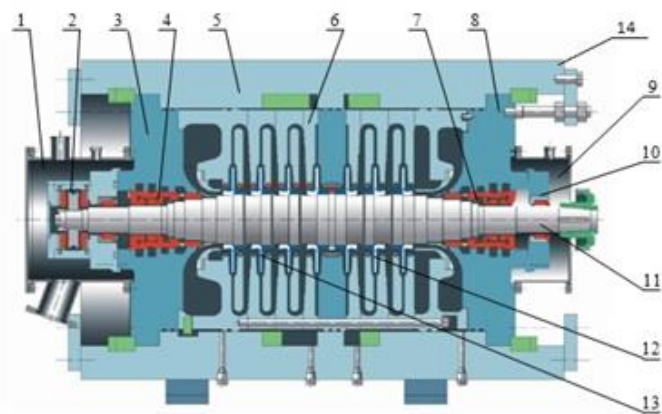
Конструкція відцентрового вакуум-компресора. 1, 9 – кожух, 2 – підшипник опорно-ударний, 3, 8 - кришка, 4, 7 - ущільнення, 5 - корпус, 6 – корпус внутрішній, 10 – підшипник опорний, 11 - ротор, 12 – робочі колеса другої секції, 13 – робочі колеса першої секції, 14 - статор
